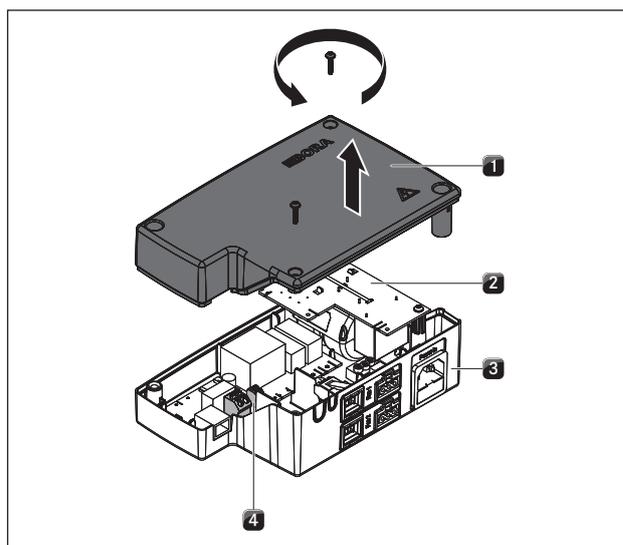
Ouvrir le couvercle de l'unité de commande universelle
